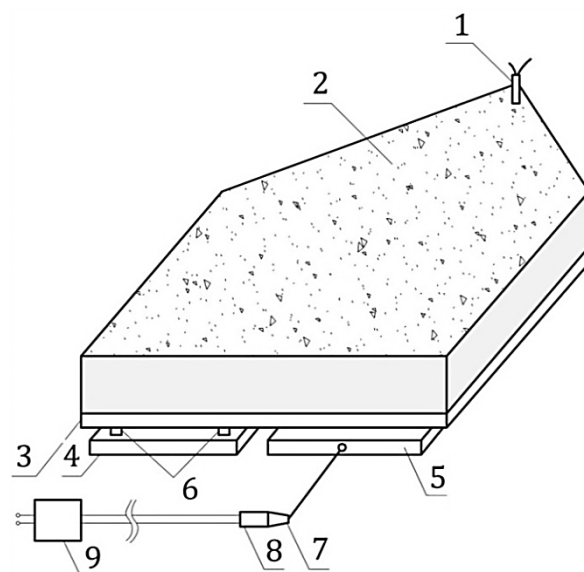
Схема сварки взрывом с воздействием ультразвука:
